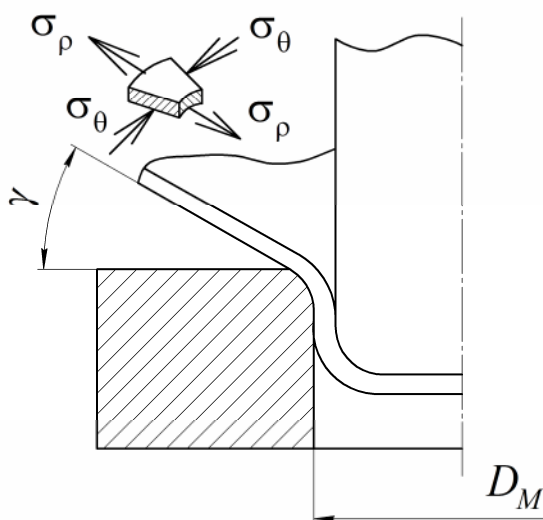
Початковий момент витяжки без притиску заготовки
